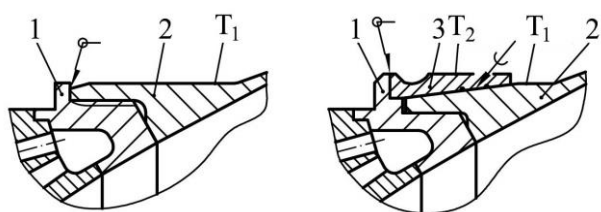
Конструкция соединения соплового насадка с охлаждаемым корпусом камеры:
